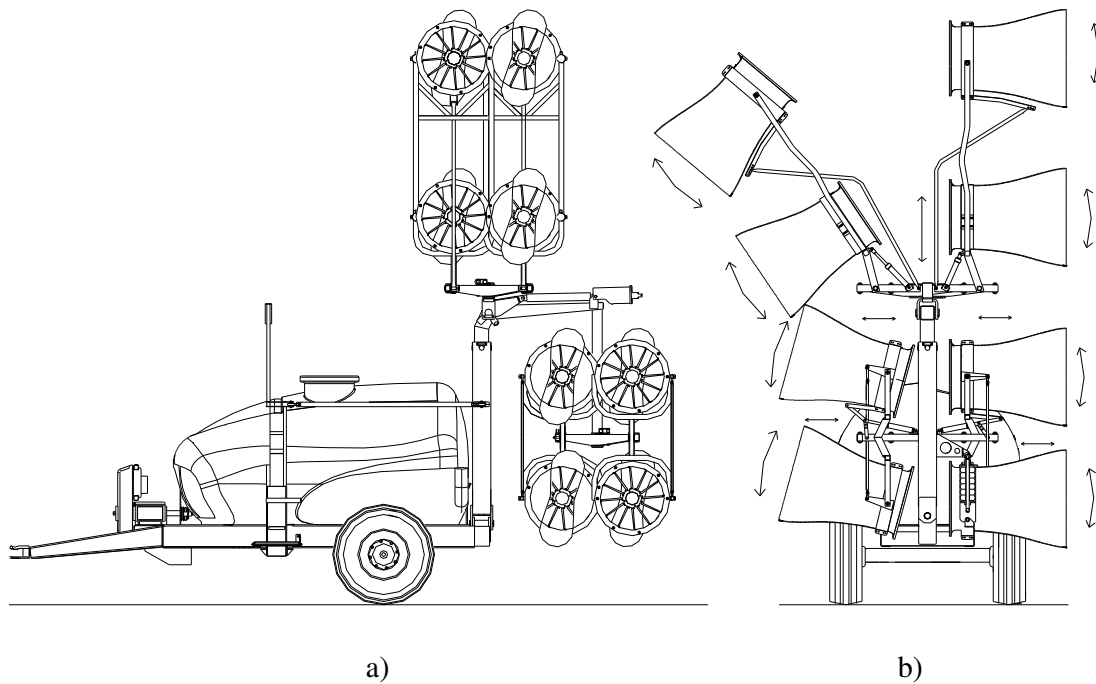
a) vista lateral e b) vista posterior do pulverizador de pomares (cortesia de Máquinas Agrícolas Jacto S/A)
